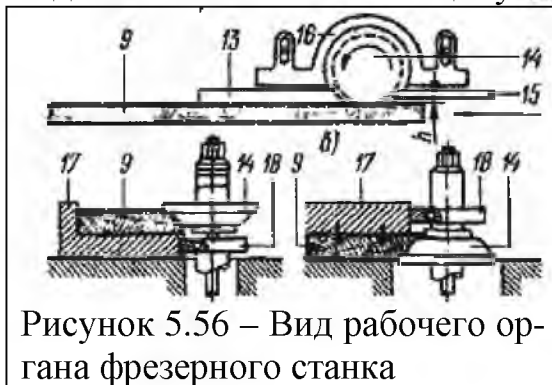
Вид рабочего органа фрезерного станка
